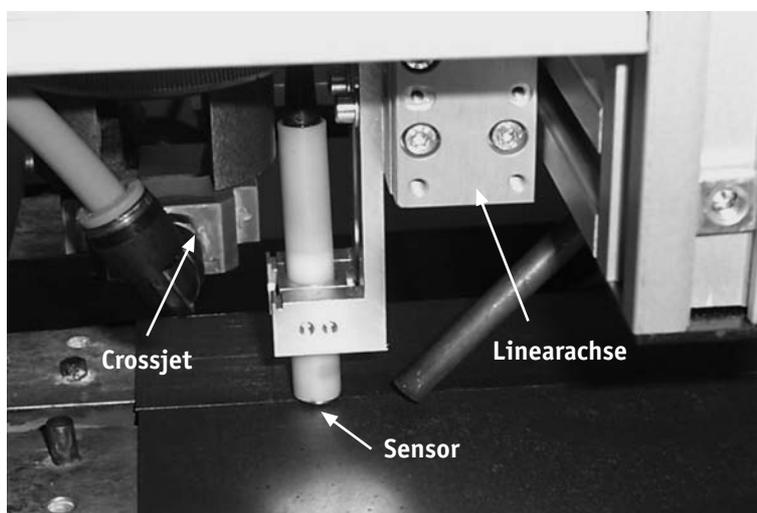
Spaltfindung mit Wirbelstromsensor im Vorlauf zum Laserschweißen
